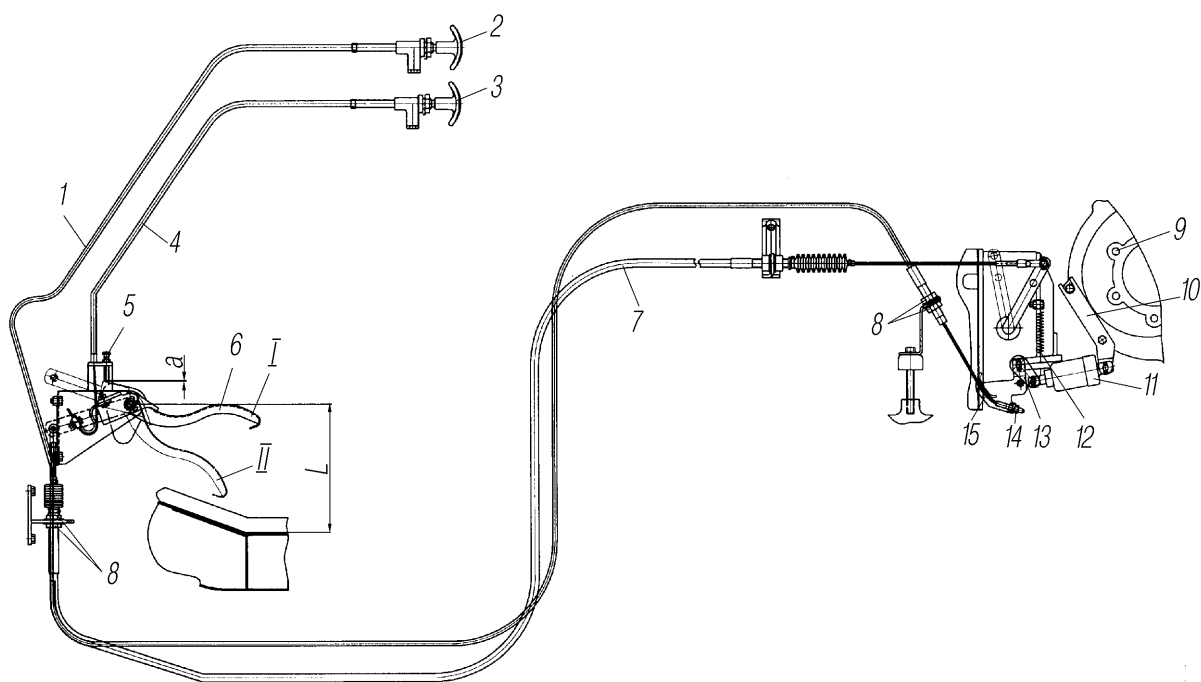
Привод управления подачей топлива и ручного останова с двигателем ЯМЗ-7511.10:
